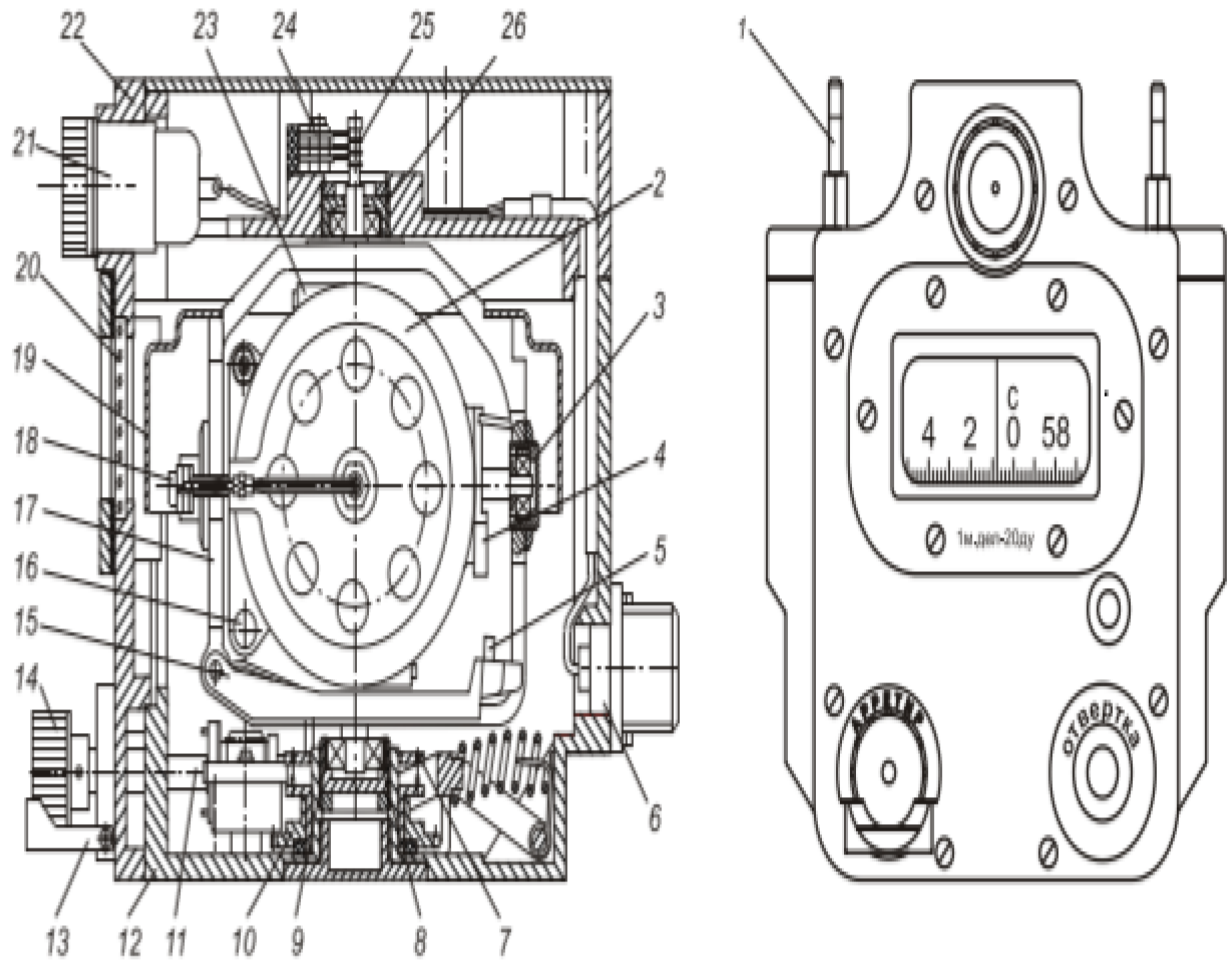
[3] Гіроскопічний показчик курсу ГПК-59: 1 - шпилька; 2 - внутрішня рамка (гірокамерой); 3 - шарікоподшипник підвісу гірокамерой; 4 - кулачок аретира; 5 - зуб коромисла аретира; 6 - вилка; 7 - кільце; 8 - магнетний шарікопідшипник; 9 - гофрована стрічка; 10 - муфта; 11 - вісь; 12 - корпус; 13 - скоба; 14 - ручка; 15 - важіль аретира; 16 - гвинт регулювальний (балансування); 17 - рамка; 18 - точковий токоподвод 19 - шкала; 20 - скло; 21 - ліхтарик; 22 - панель; 23 - сопло; 24 - вузол щіток; 25 - колектор; 26 - втулка різьбова.
